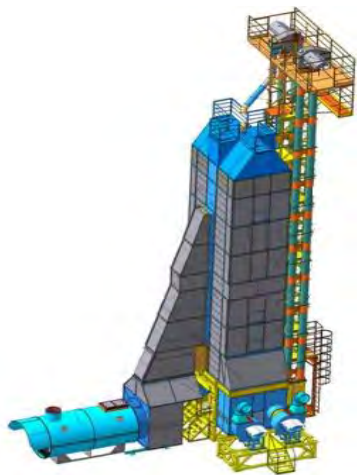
Загальний вигляд сушарки СЗШМ-30
